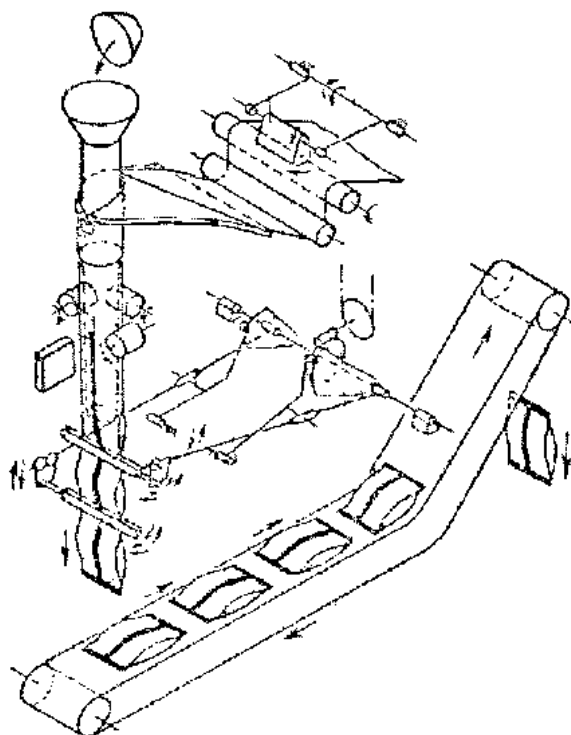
Схема агрегату з комірцем періодичної дії типу АРЖ, формує вигляд упоковки типу «подушечка»
